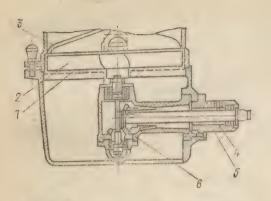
Проторочный механизм МУ-1000 (модель 723-7М)
